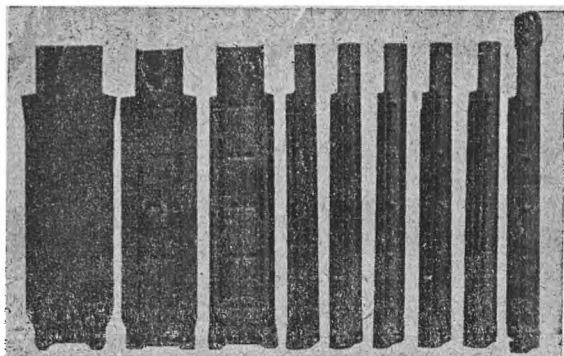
Armatka samolotowa kal. 30 mm. w konstrukcji tłoczonej.
